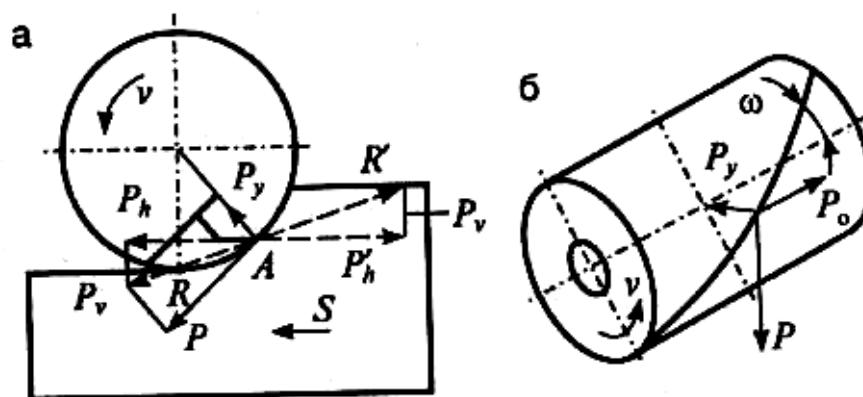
Силы резания при работе цилиндрической фрезой:
